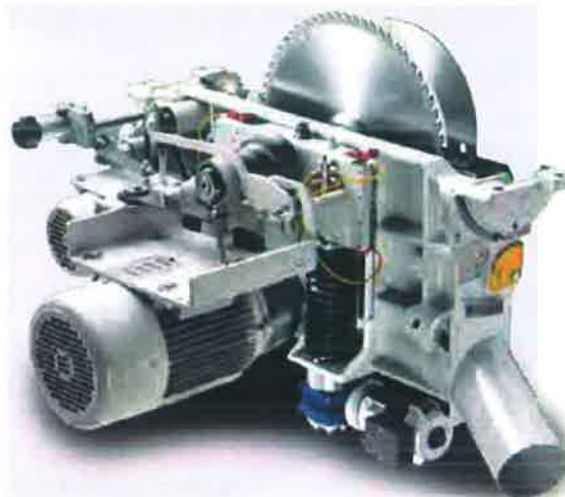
Widok pilarki UNICA 400 firmy Griggio, [3].
